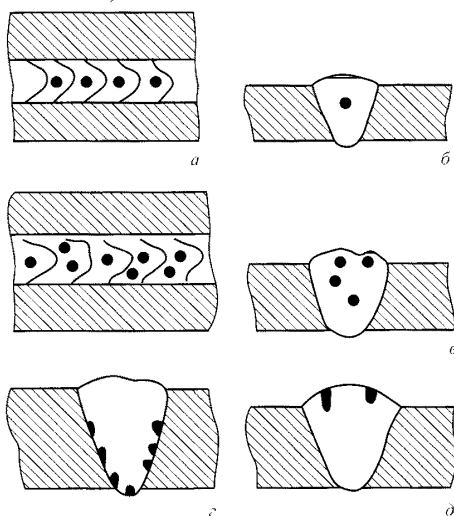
Поры в сварном шве: а – цепочка; б – единичные; в, г – скопления; д – свищи
